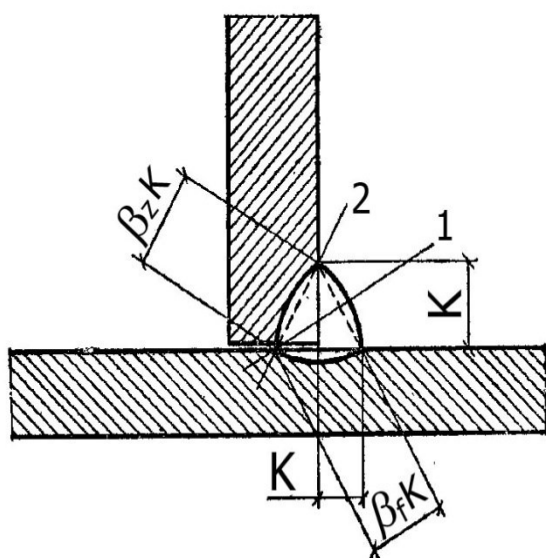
Схема расчетных сечений сварного соединения с угловым швом: 1 — сечение по металлу шва; 2 — сечение по металлу границы сплавления
